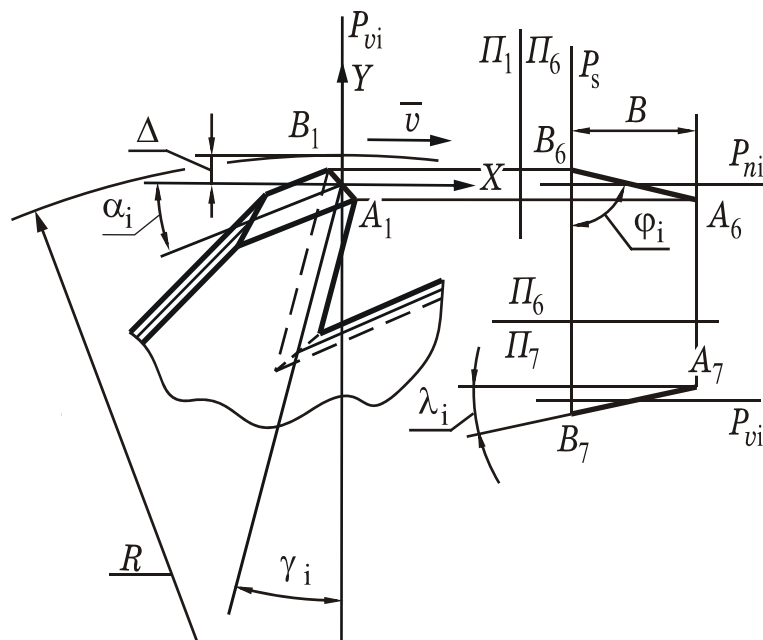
Інструментальні геометричні параметри зуба відрізної фрези
